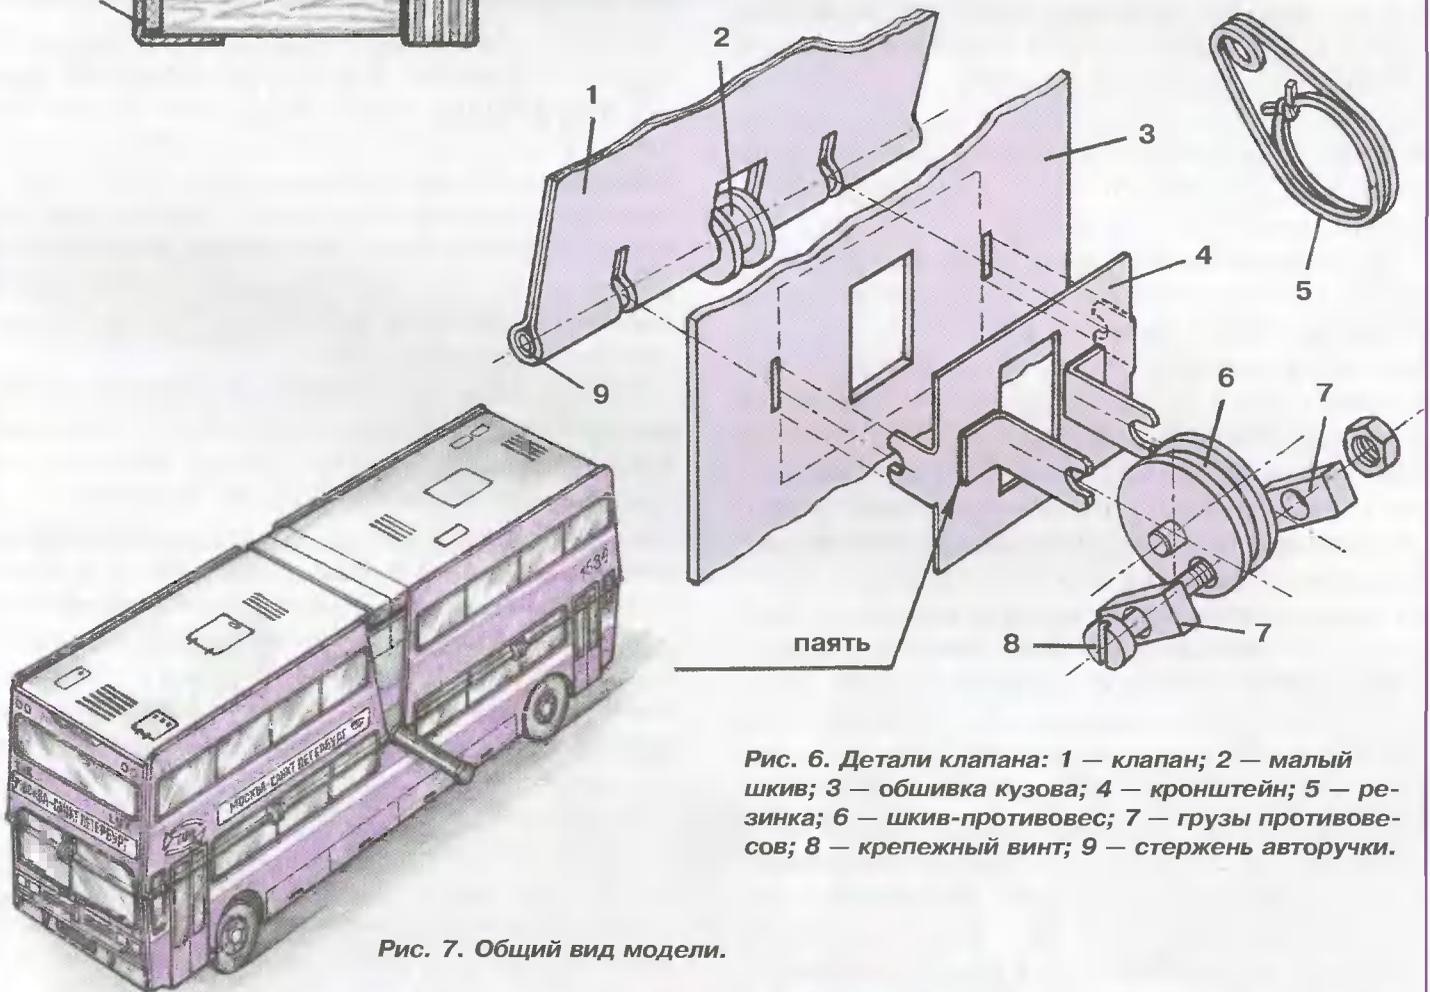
Детали клапана: 1 — клапан; 2 — малый шкив; 3 — обшивка кузова; 4 — кронштейн; 5 — резинка; 6 — шкив-противовес; 7 — грузы противовесов; 8 — крепежный винт; 9 — стержень авторучки.
